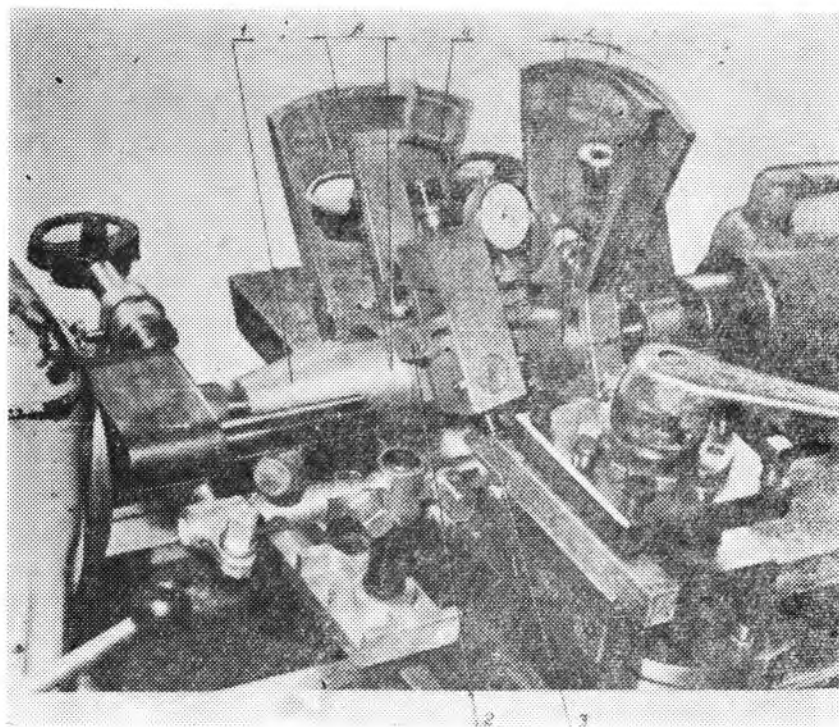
Установка для проверки жесткости узлов токарного станка:
